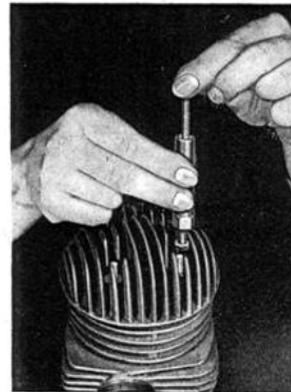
Erleichterung des Anfüdelns der Mutter auf die Zylinderstehbolzen bei RT-Modellen: Benutzung einer langen Schraube, auf die die Mutter mit 1-2 Gängen aufgeschraubt wird und die gleichzeitig als Führung für den Steckschlüssel dient. Besonders zu empfehlen beim Arbeiten am nicht ausgebauten Motor
